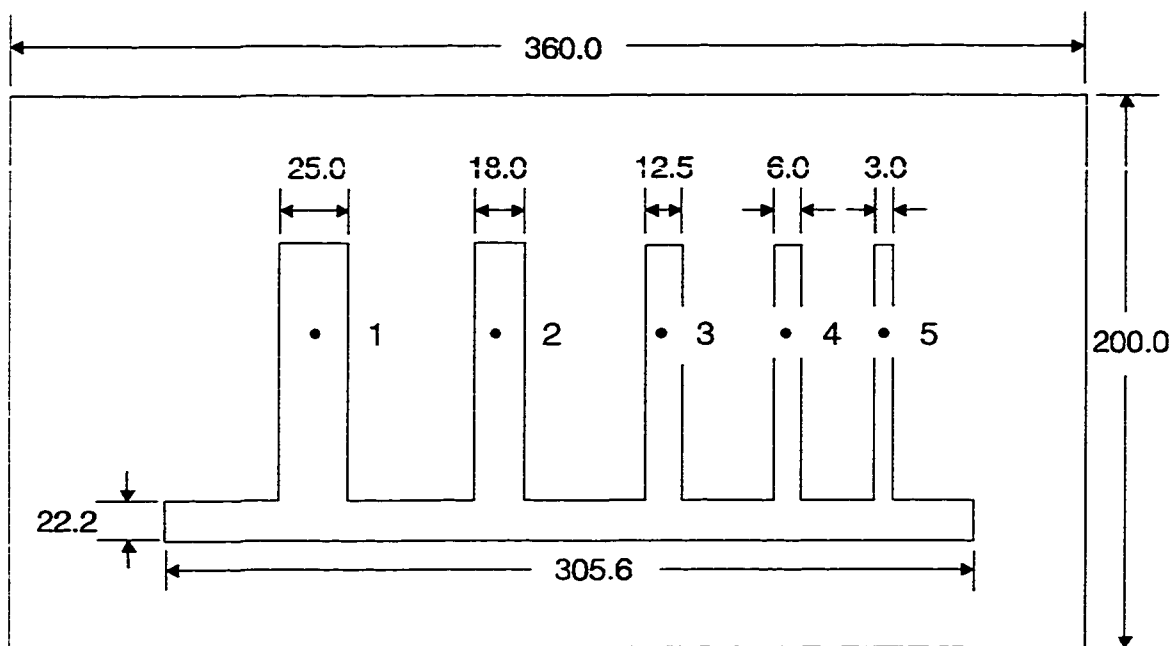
Dimensions des composantes pièce-moule pour la solidification étagée
